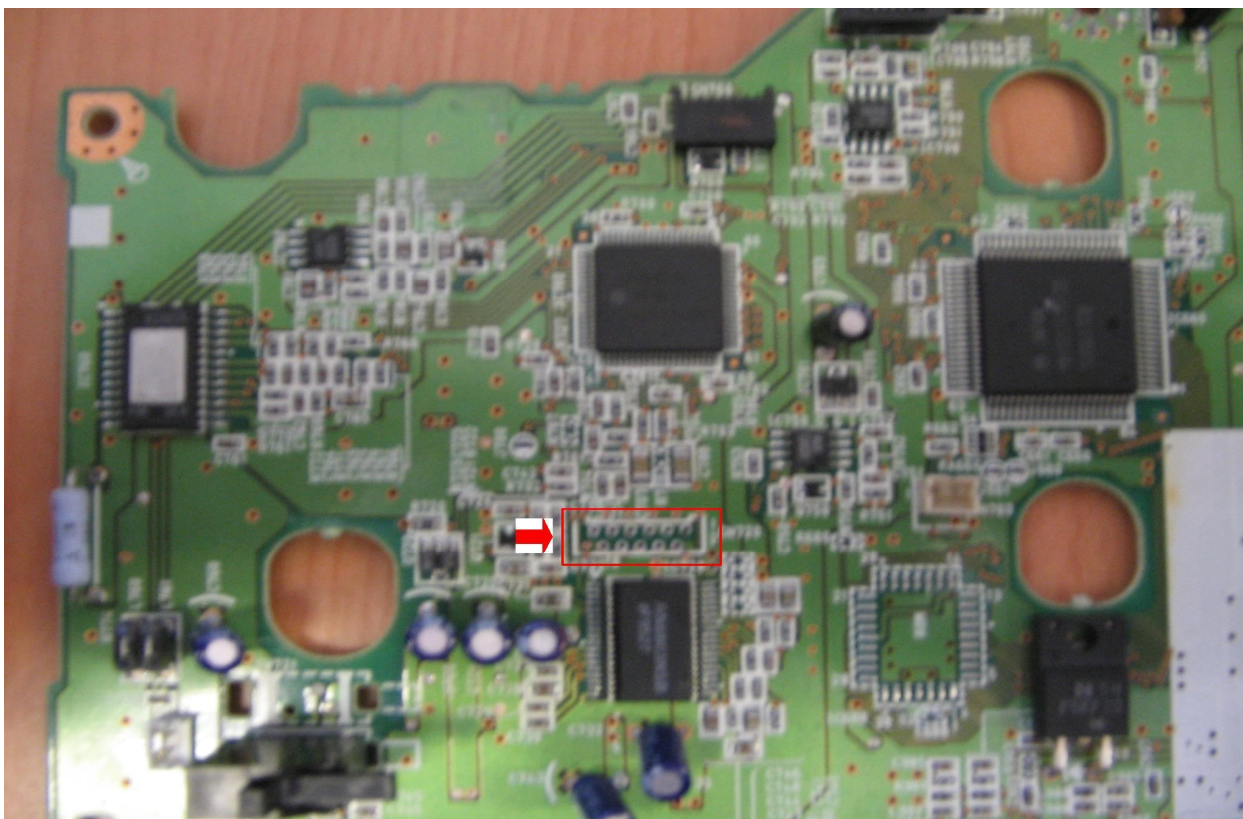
Стыковка 11 – контактного шлейфа. Шаг 1.
